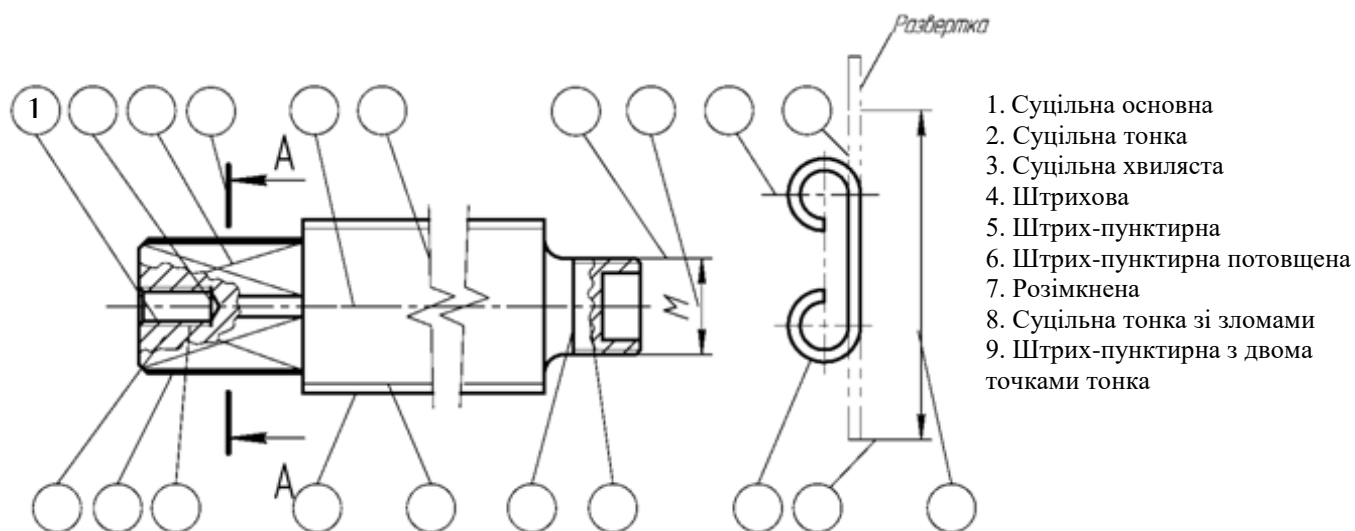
Креслення деталі для вибору нумерації типів ліній
